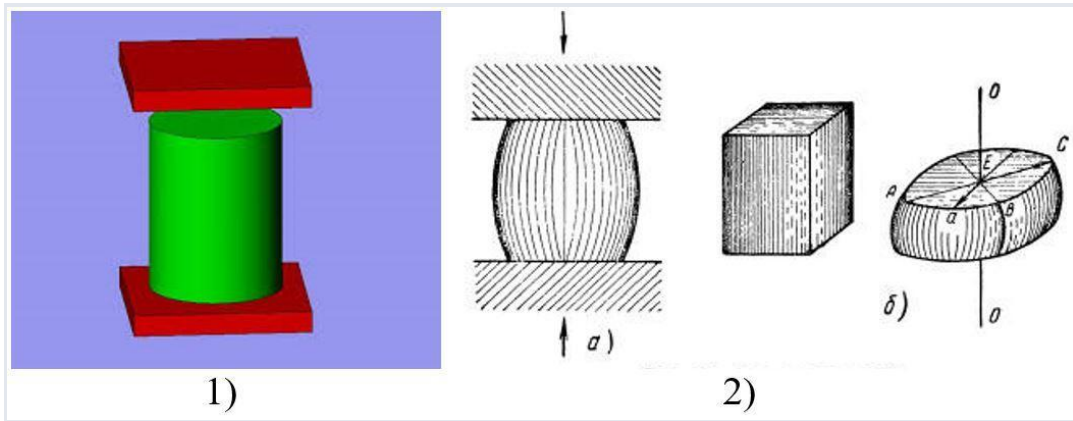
Осадка заготовки: 1) модель процесу; 2) види форм заготовки: а) циліндричної- бочкоподібної; б) квадратної
